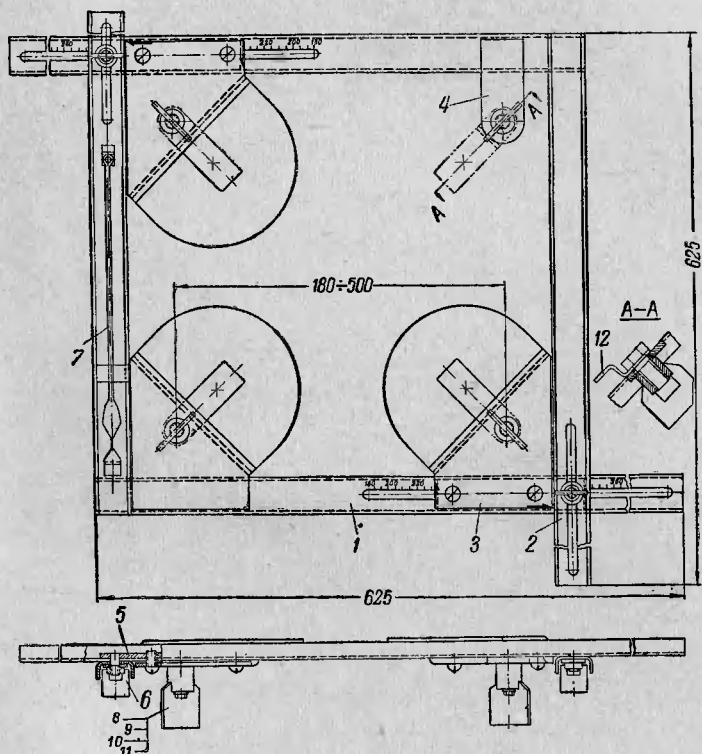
Универсальный кондуктор для разметки и пристрелки.
